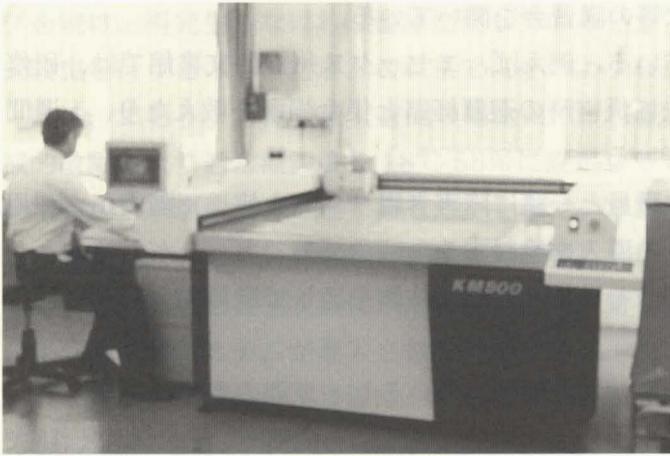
スコットランド国立図書館のBox-making machine (箱製造装置)
